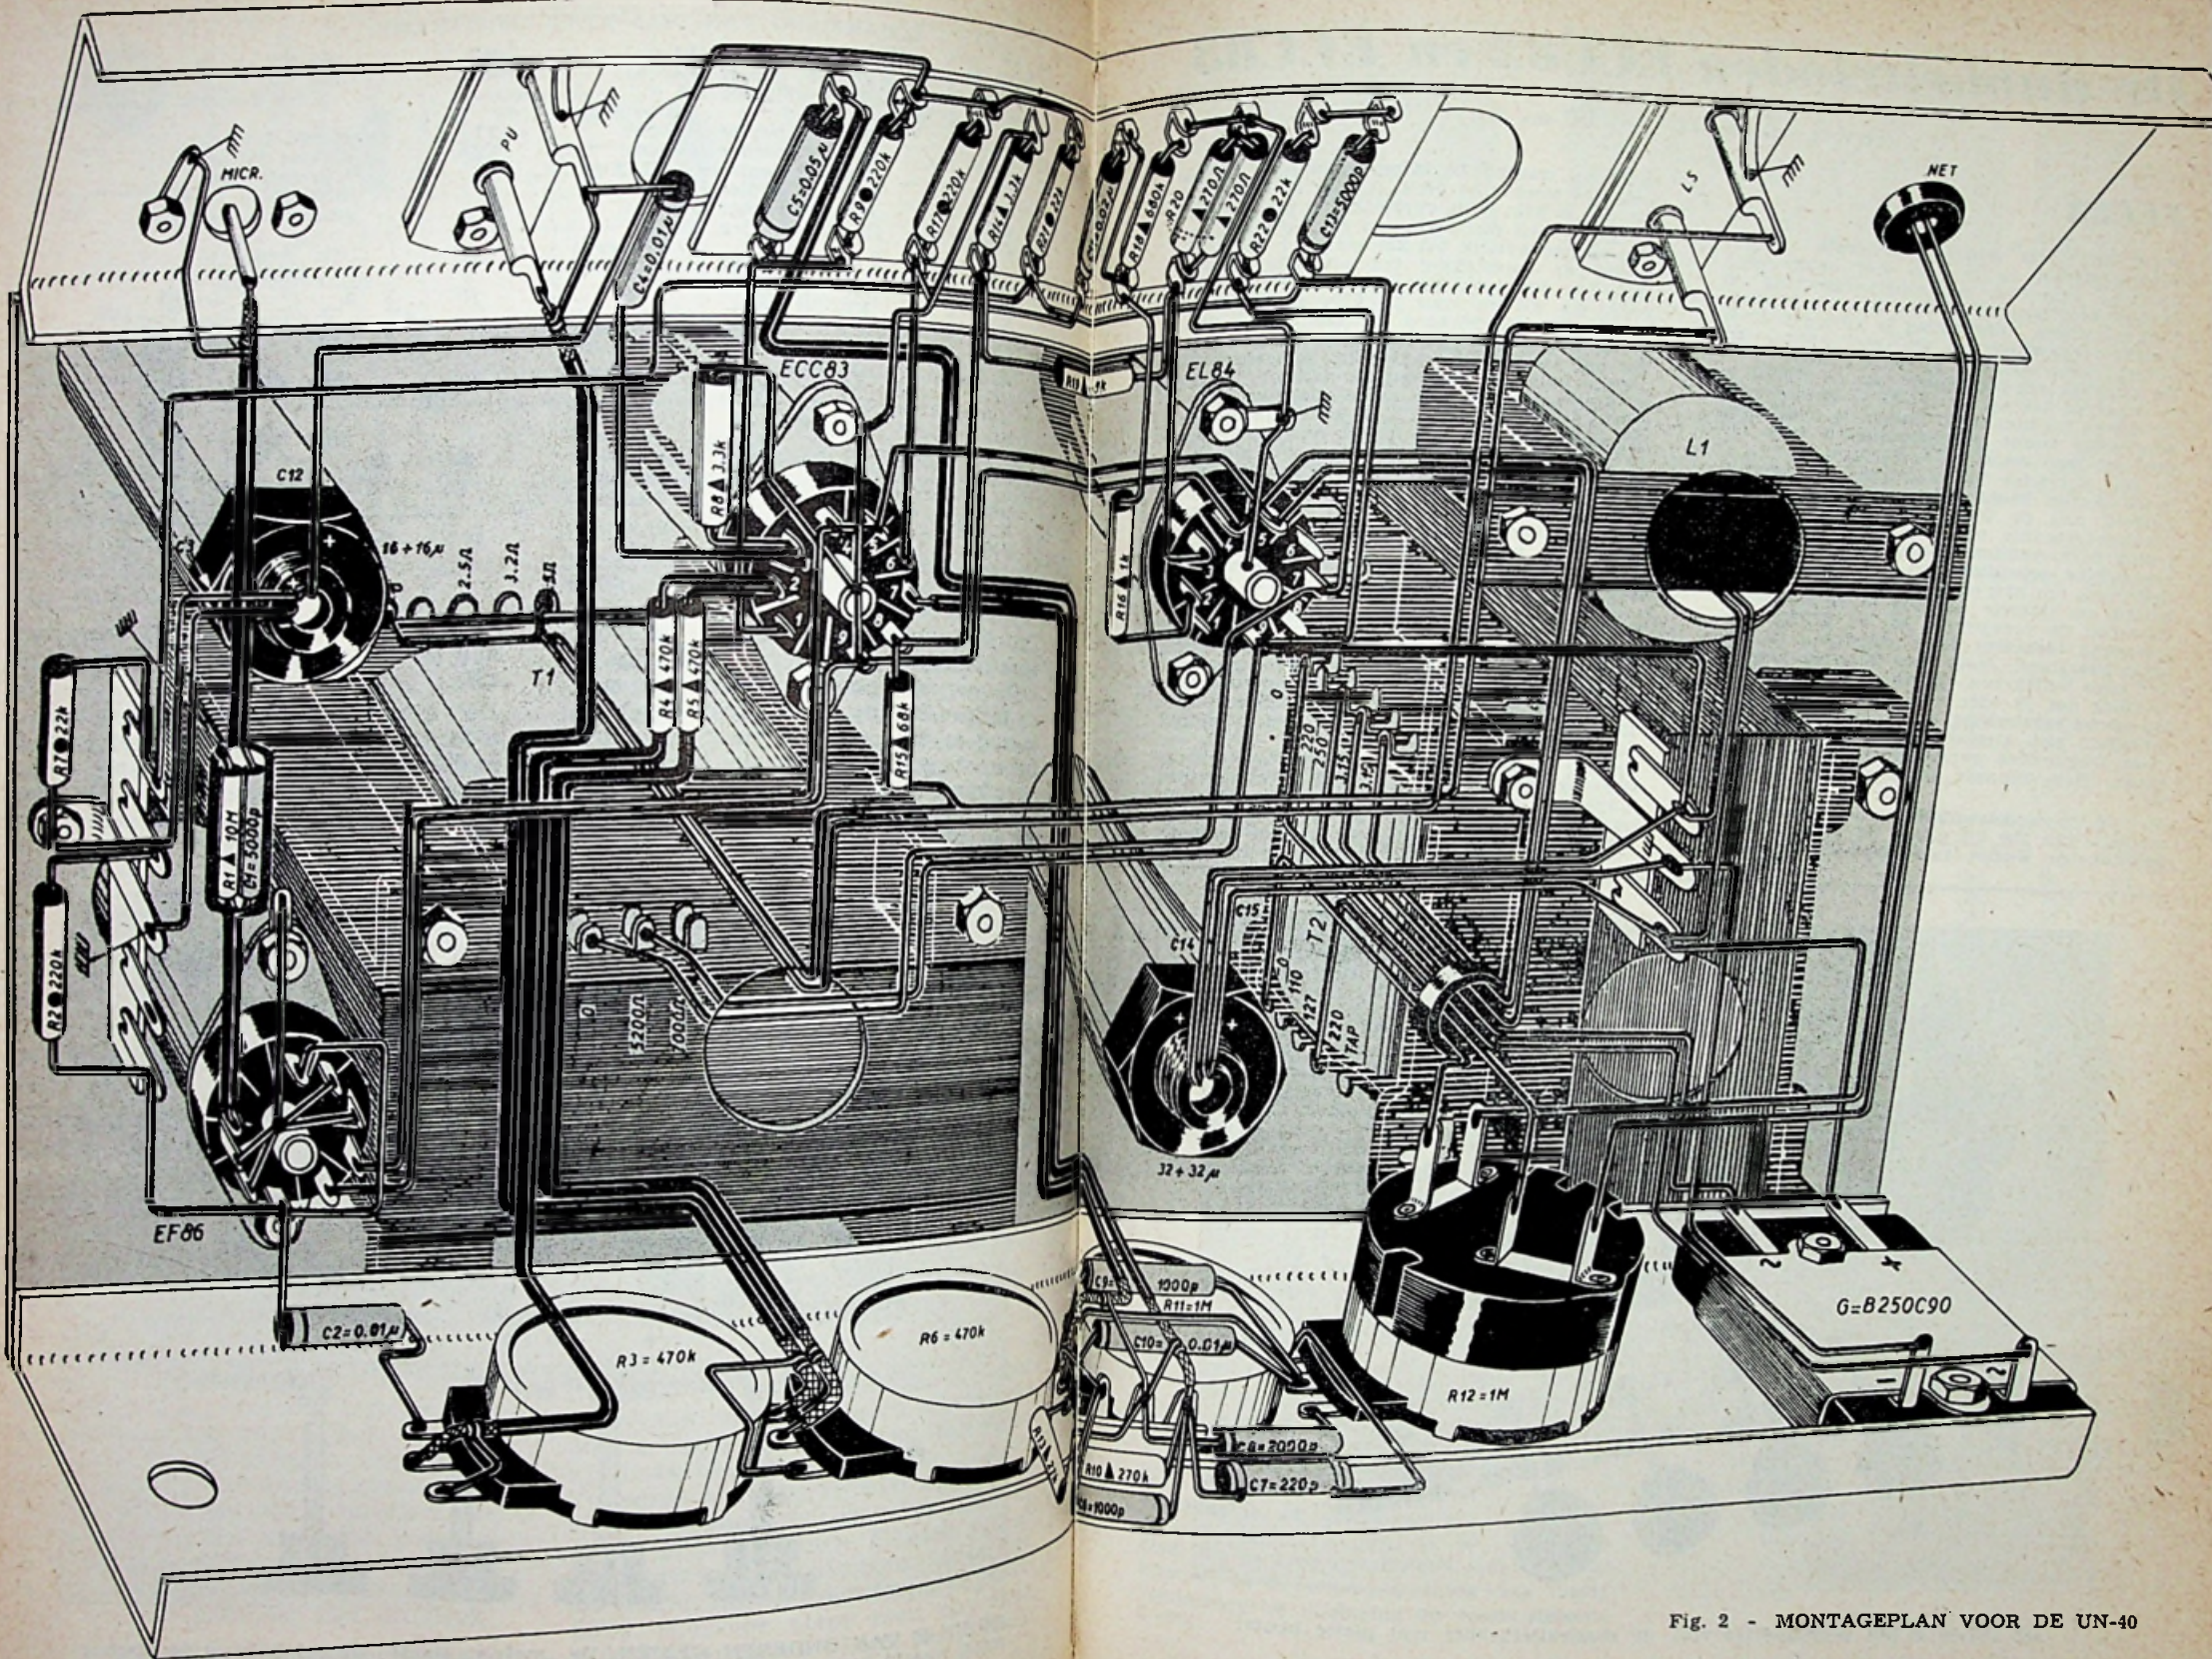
MONTAGEPLAN VOOR DE UN-40
